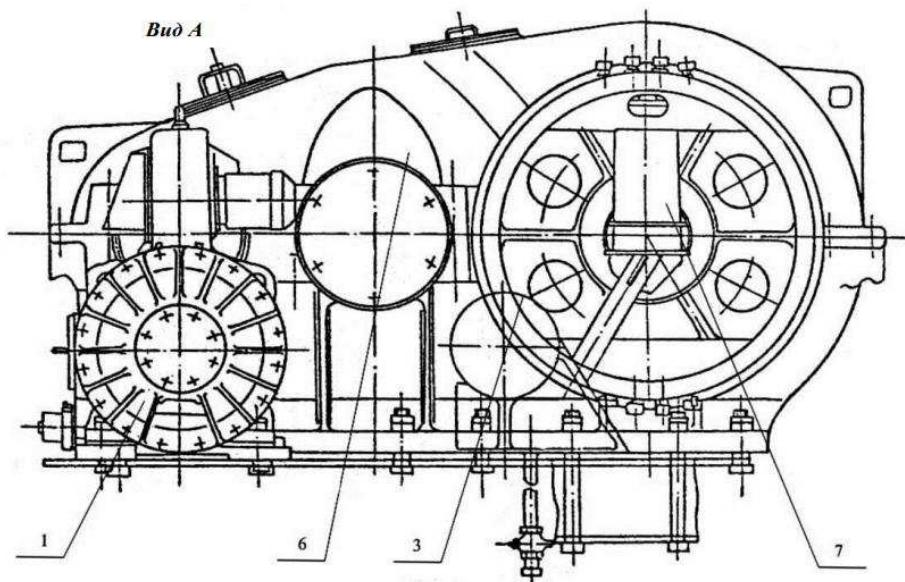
Лебедка напора (вид сбоку)
